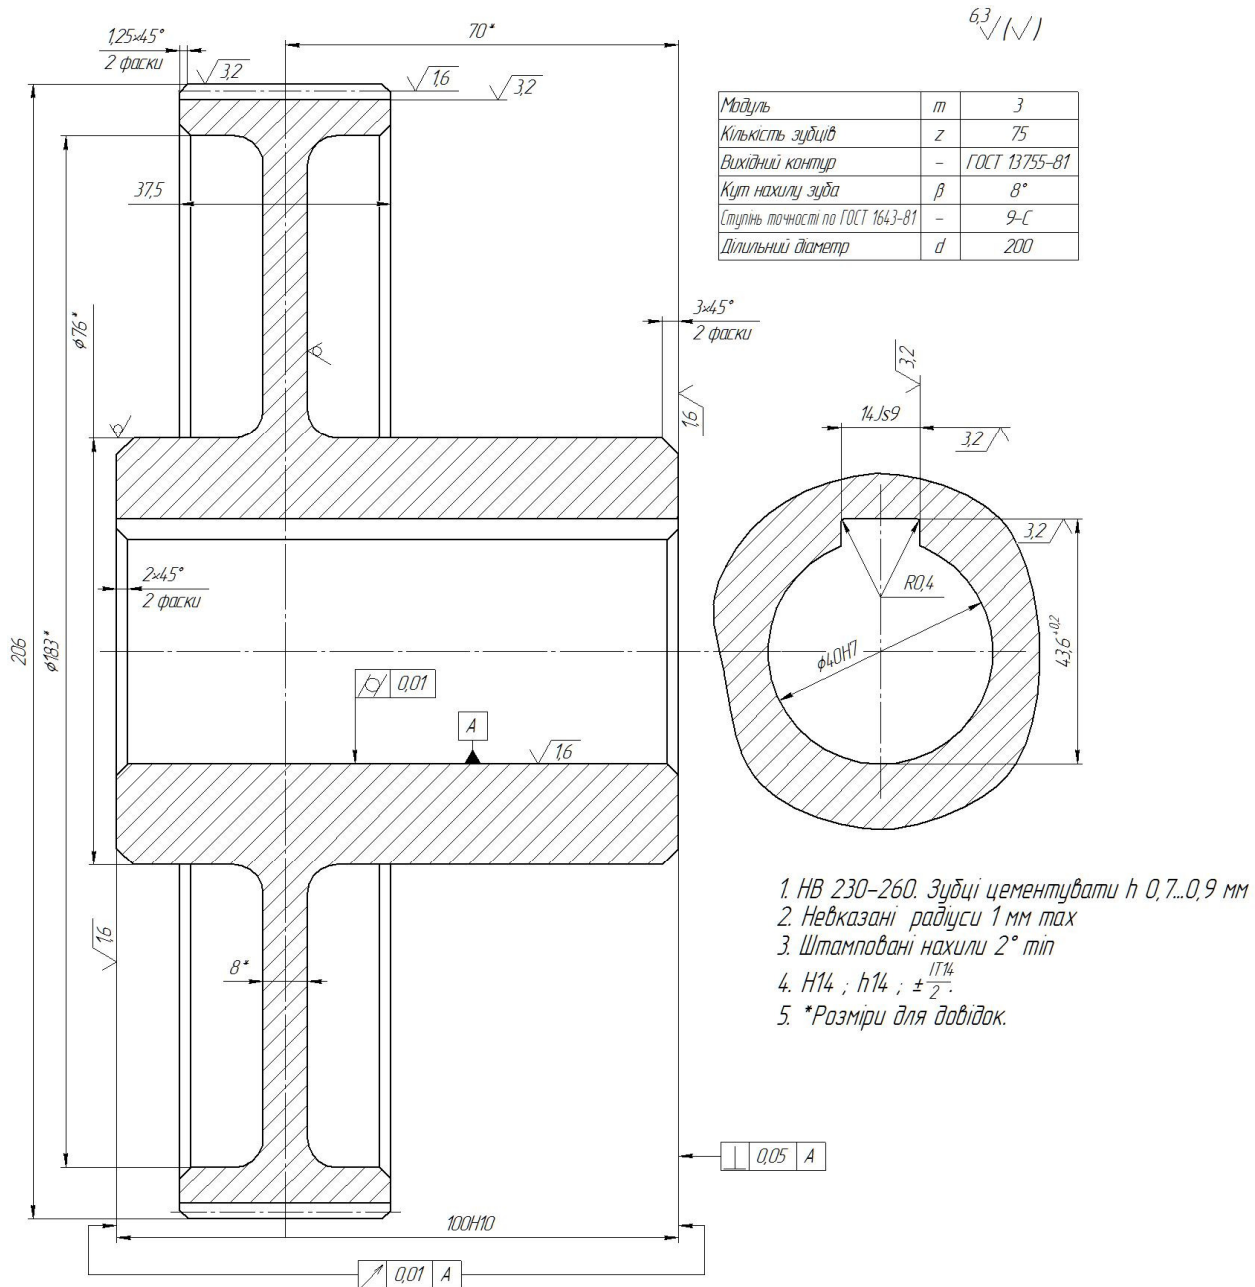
Кресленик колеса зубчастого (Сталь 40X)
